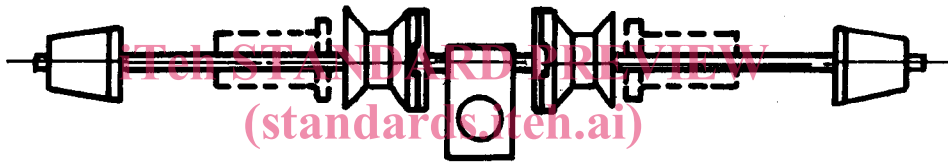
Type 6 — Guindeau symétrique à deux barbotins et à tambour à câble¹⁾
